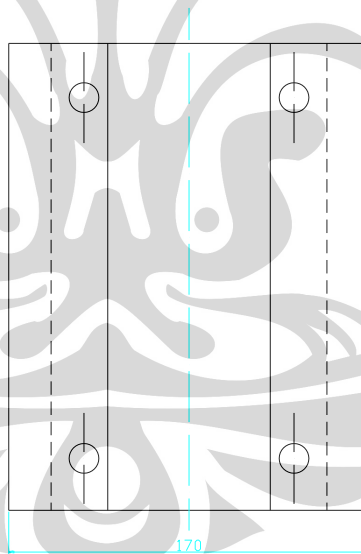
Rel *securing fitting* 3 dimensi (sketsa)
